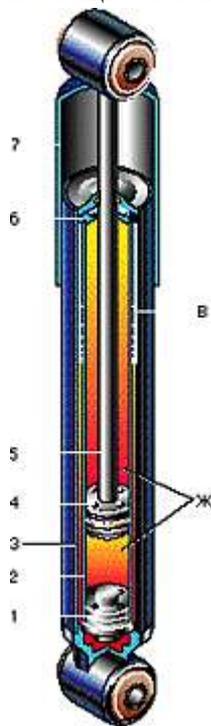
Схема гидравлического двухтрубного амортизатора*: 1- клапан сжатия; 2 — рабочий цилиндр; 3 — цилиндр резервуара; 4 — поршень и клапан отбоя; 5 — шток; 6 — уплотняющий и направляющий узел штока; 7 — кожух; Ж — жидкость; В — воздух.
